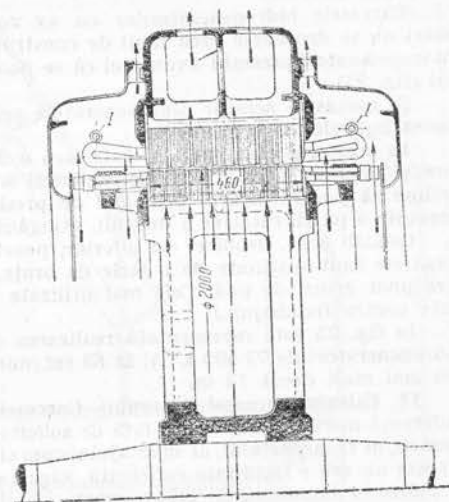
Motor asincron având carcasa turnată cu scuturi și suport inelar pentru capetele de bobină.
